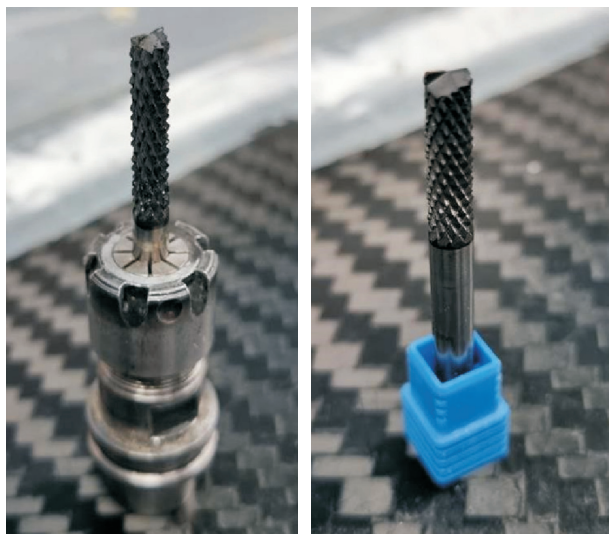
Внешний вид концевых фрез P0801060002500D00 фирмы AXIS (а) и 870060.0 компании SECO (б)
